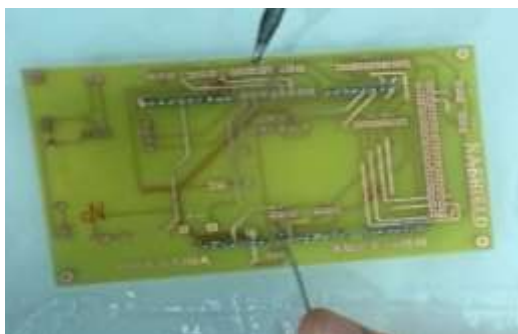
Différentes phases d'assemblage et de soudage manuel du Shield
